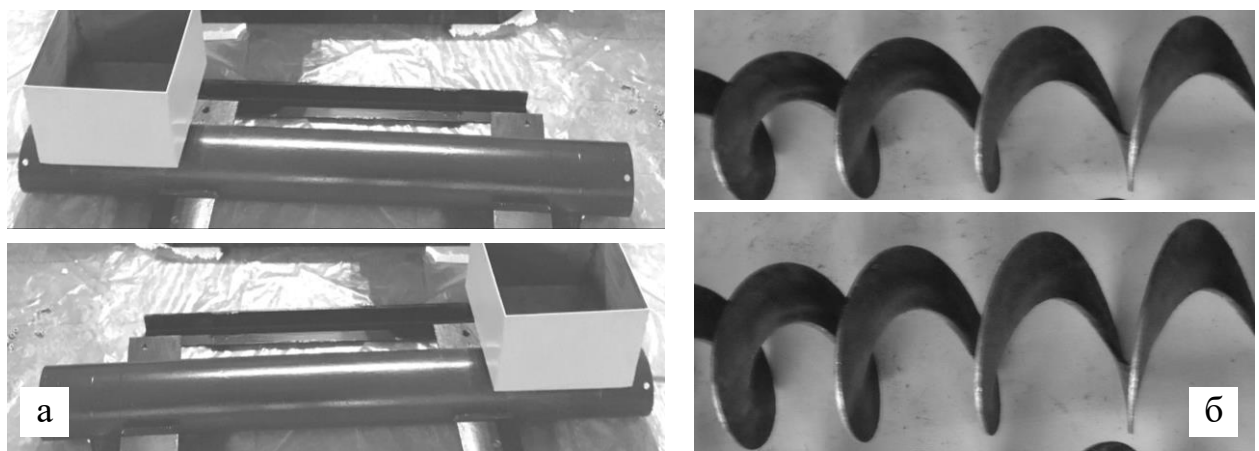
Загальний вигляд: а – змінні кожухи; б – спіральні заготовки
